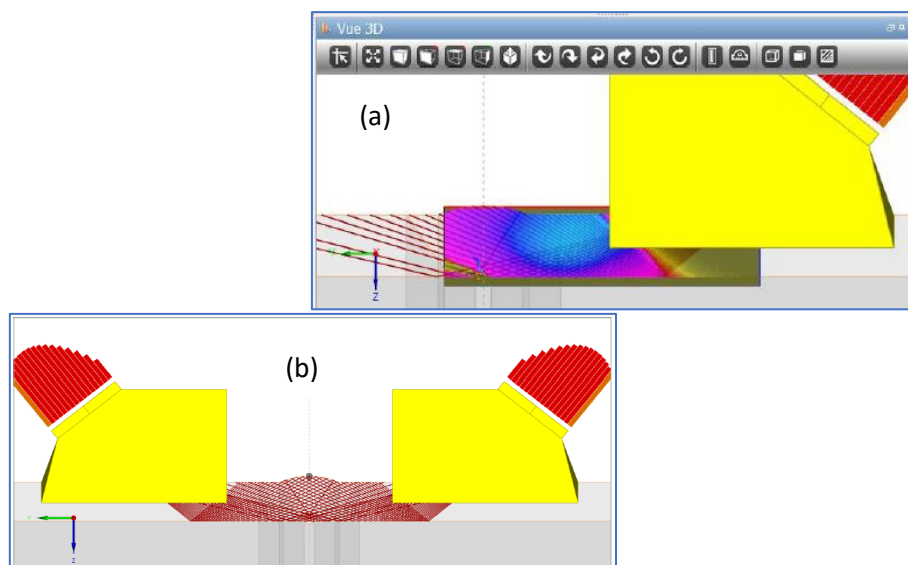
Couverture de zone en mono-élément et PA pour un assemblage tube/tube de DN60.3mm
